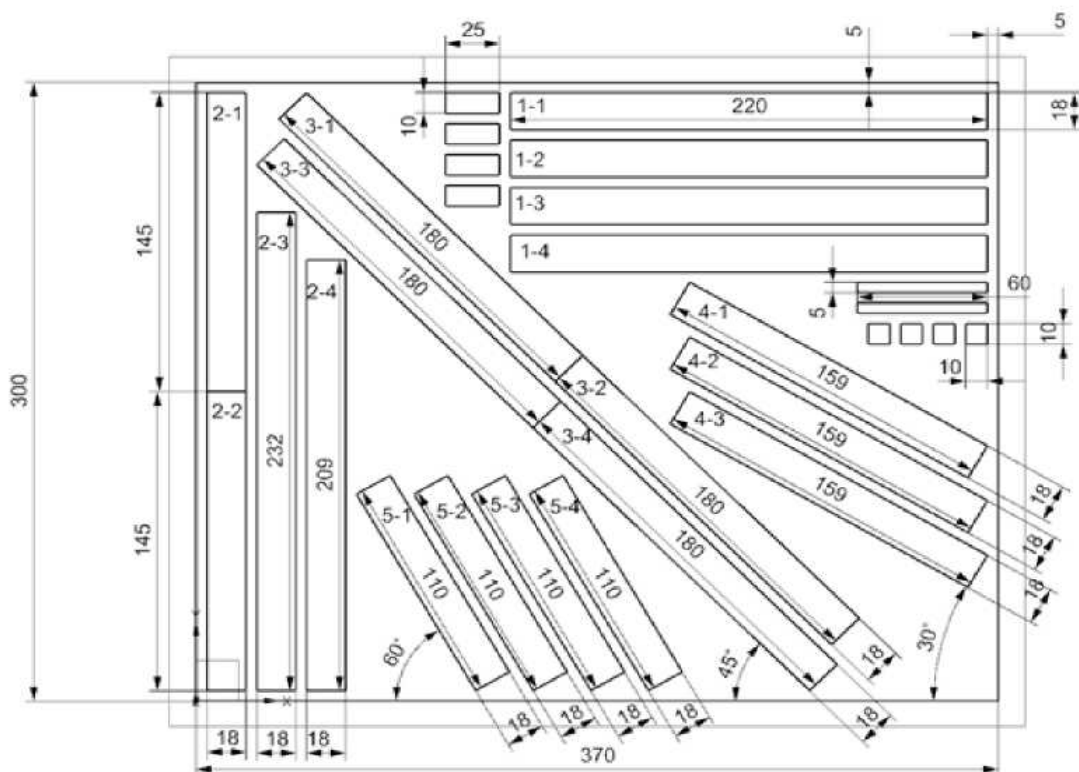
Схема раскроя пластины из углепластика БМИ-3/3692
